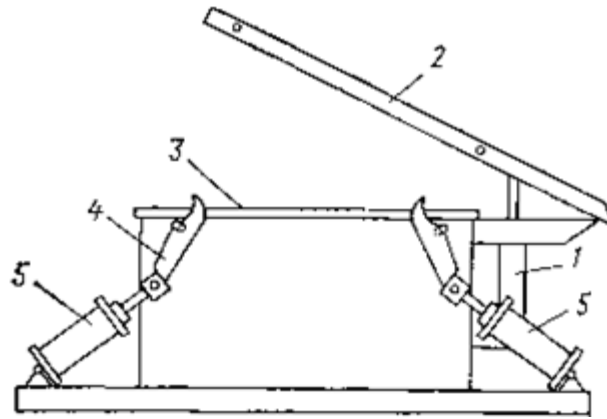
Затискна рама з різними циліндрами для її підйому вичавлива заготовки
